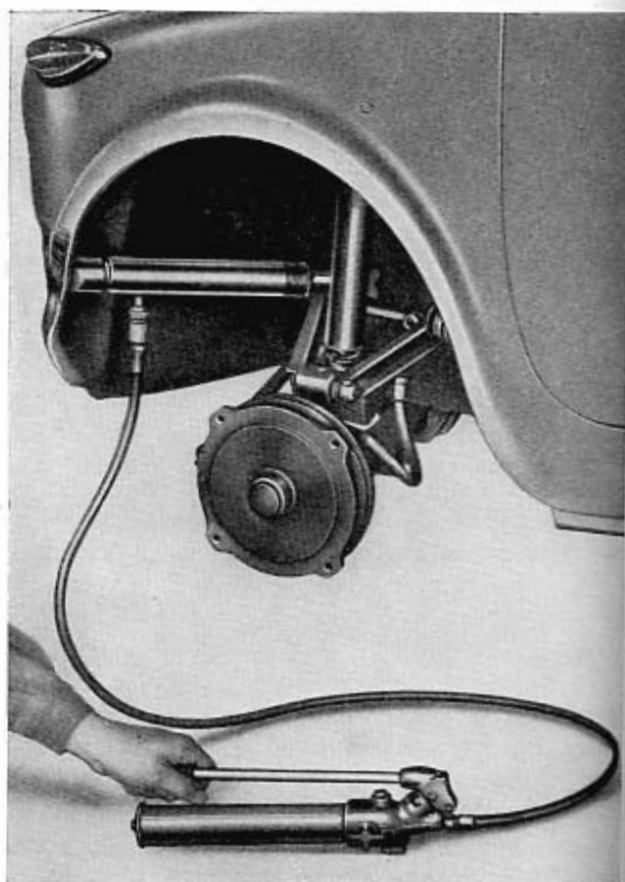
Application du cric hydraulique pour redresser la partie avant de la carrosserie.
